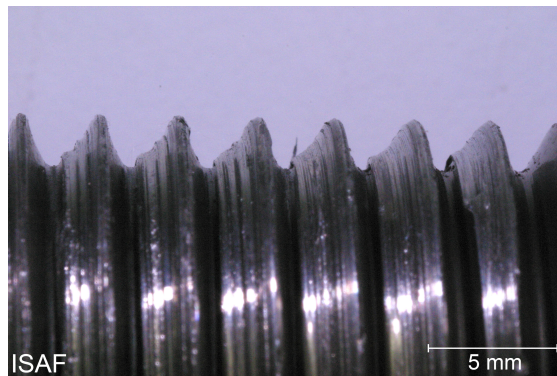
Gewindeprüfkörper axial belastet mit 80kN (Bolzen)
